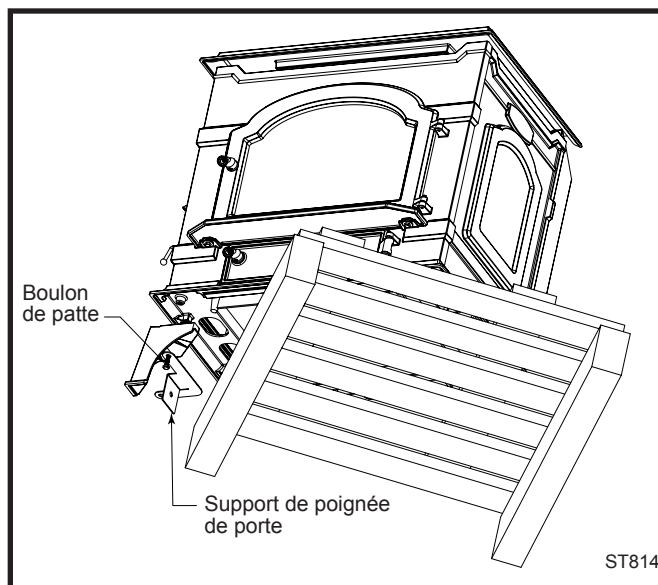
Tournez le poêle sur la palette pour exposer le coin avant gauche.
